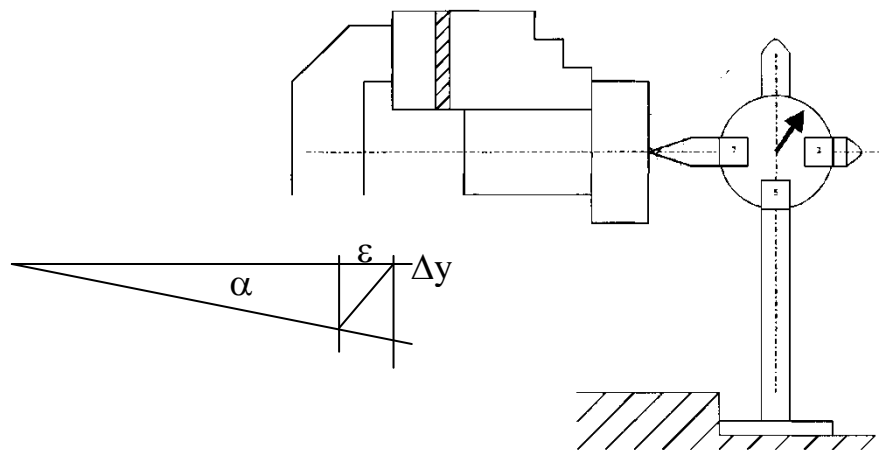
Схема установки индикатора для определения осевой погрешности закрепления заготовки.
